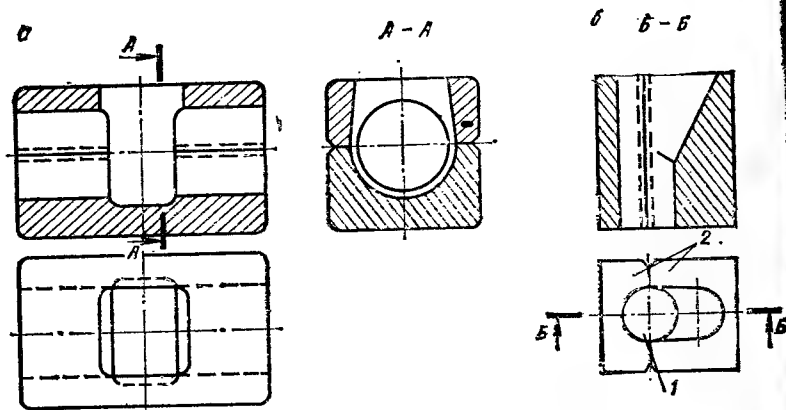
Конструкция призматических инвентарных медных форм для ванной сварки стыковых соединений однорядных стержней
